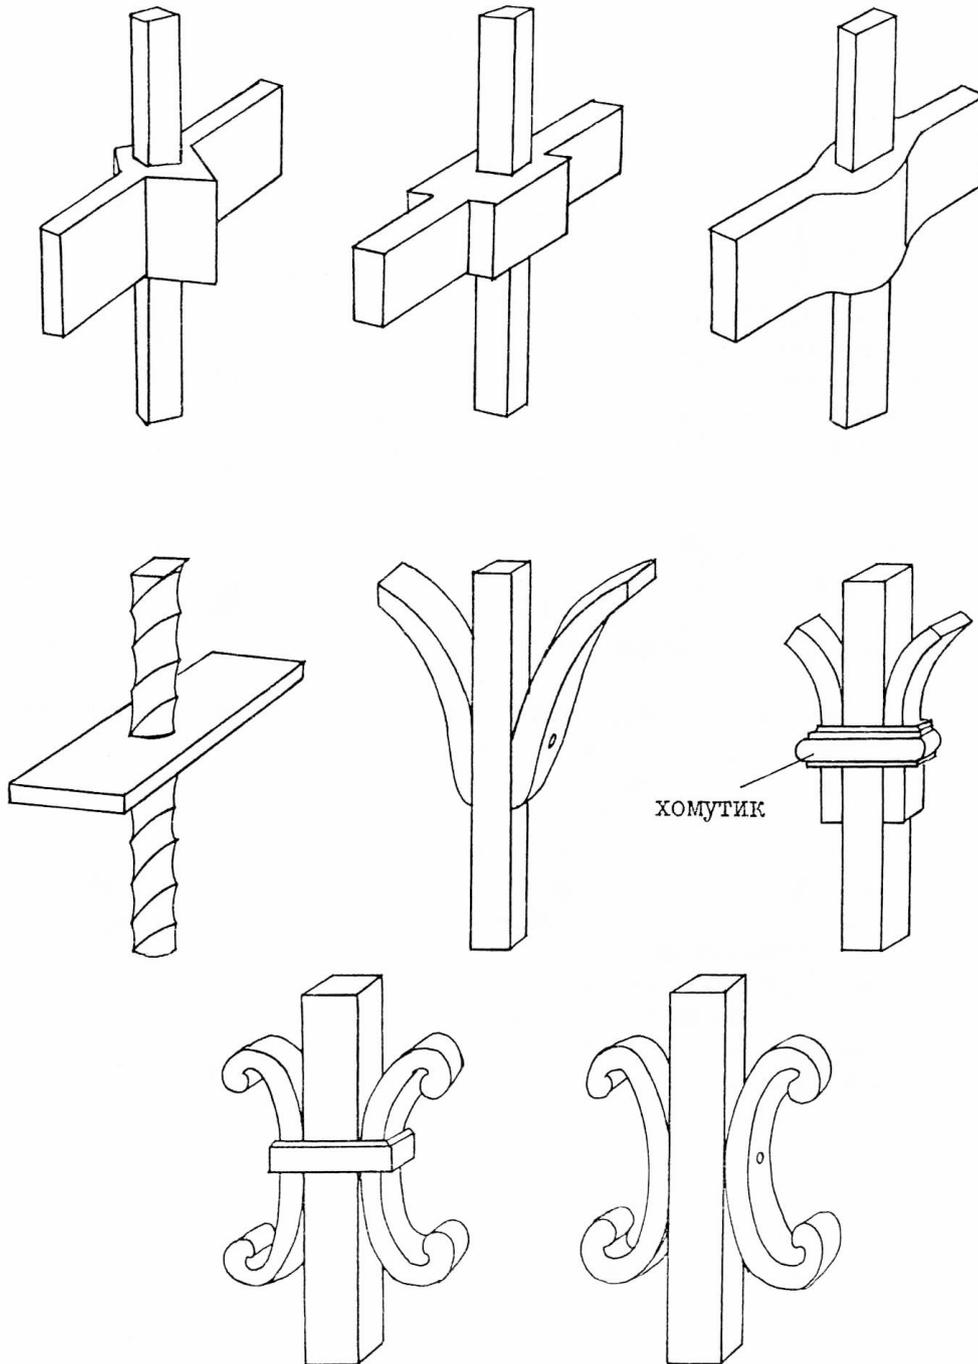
З'єднання деталей огорож за допомогою ковальського (горнового) зварювання
